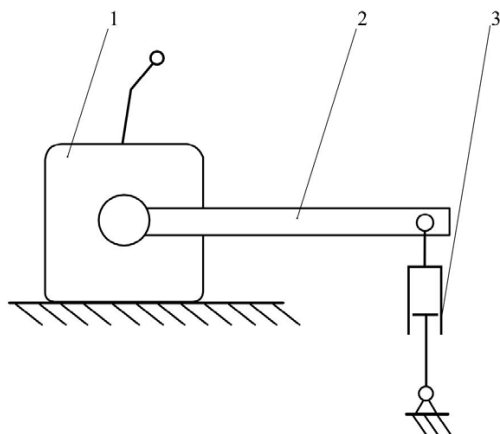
Принципиальная схема стенда для определения статической прочности коробки передач: 1 – испытываемая коробка передач; 2 – рычаг; 3 – нагружающее устройство
